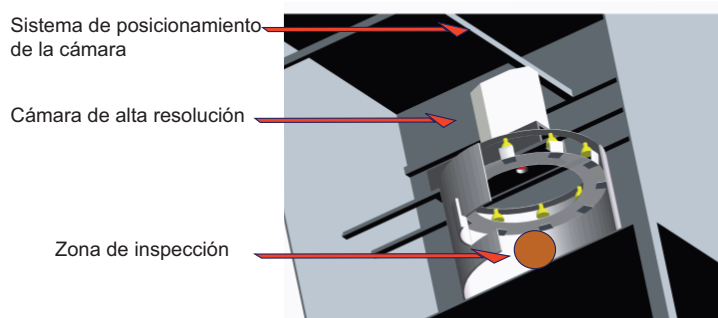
Diseño de la campana de iluminación cilíndrica y su alojamiento en la campana de inspección.
